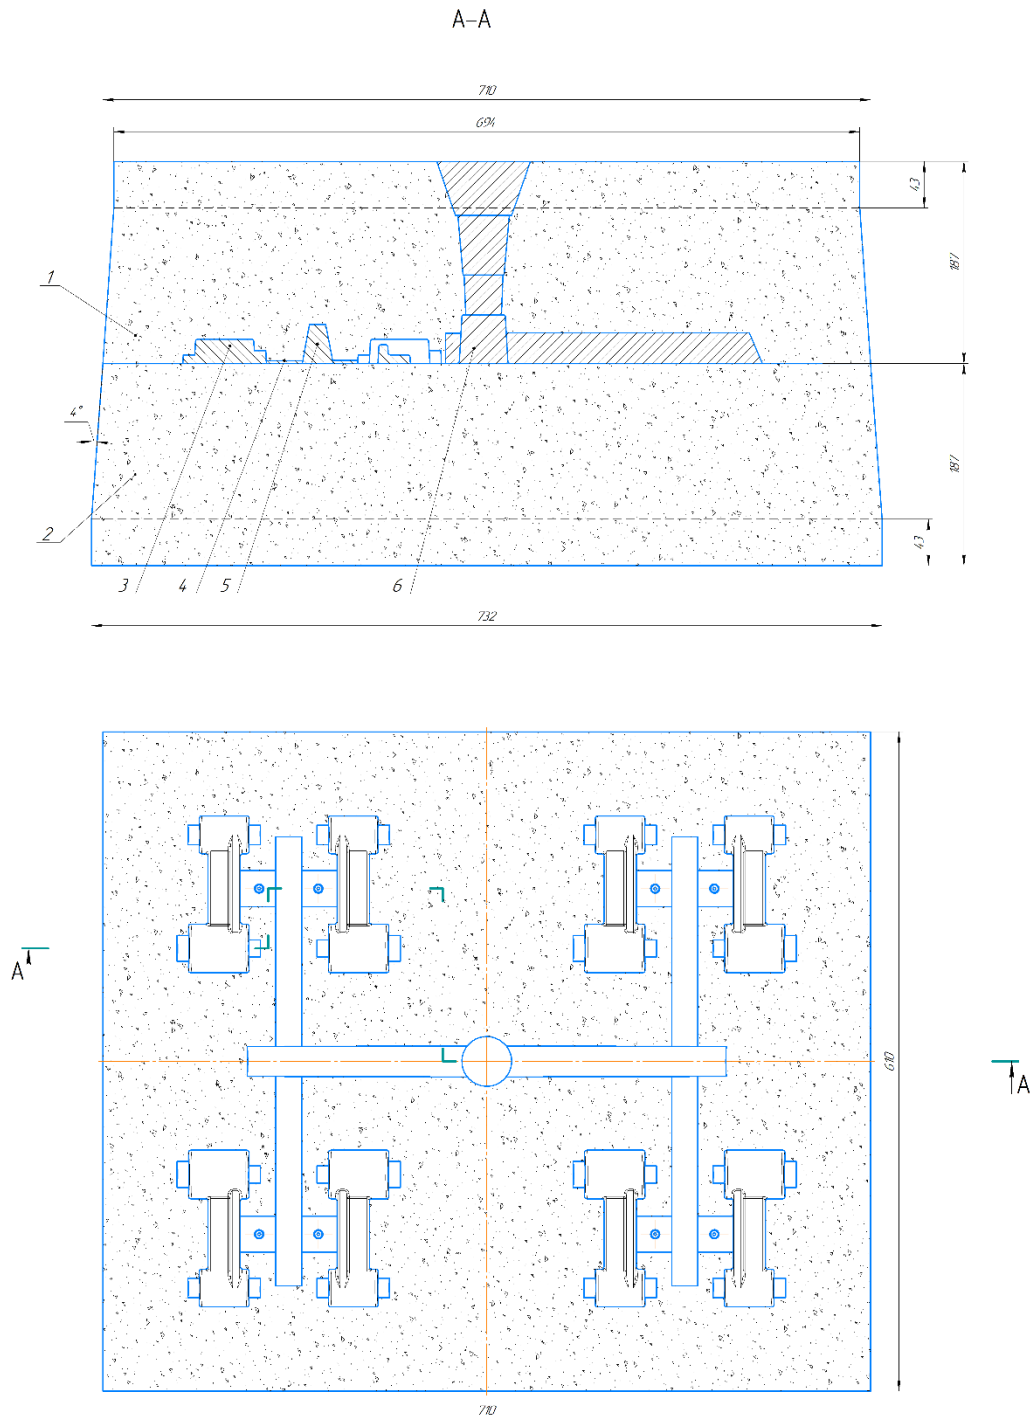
Ливарна форма для виготовлення відливків «Важіль»
